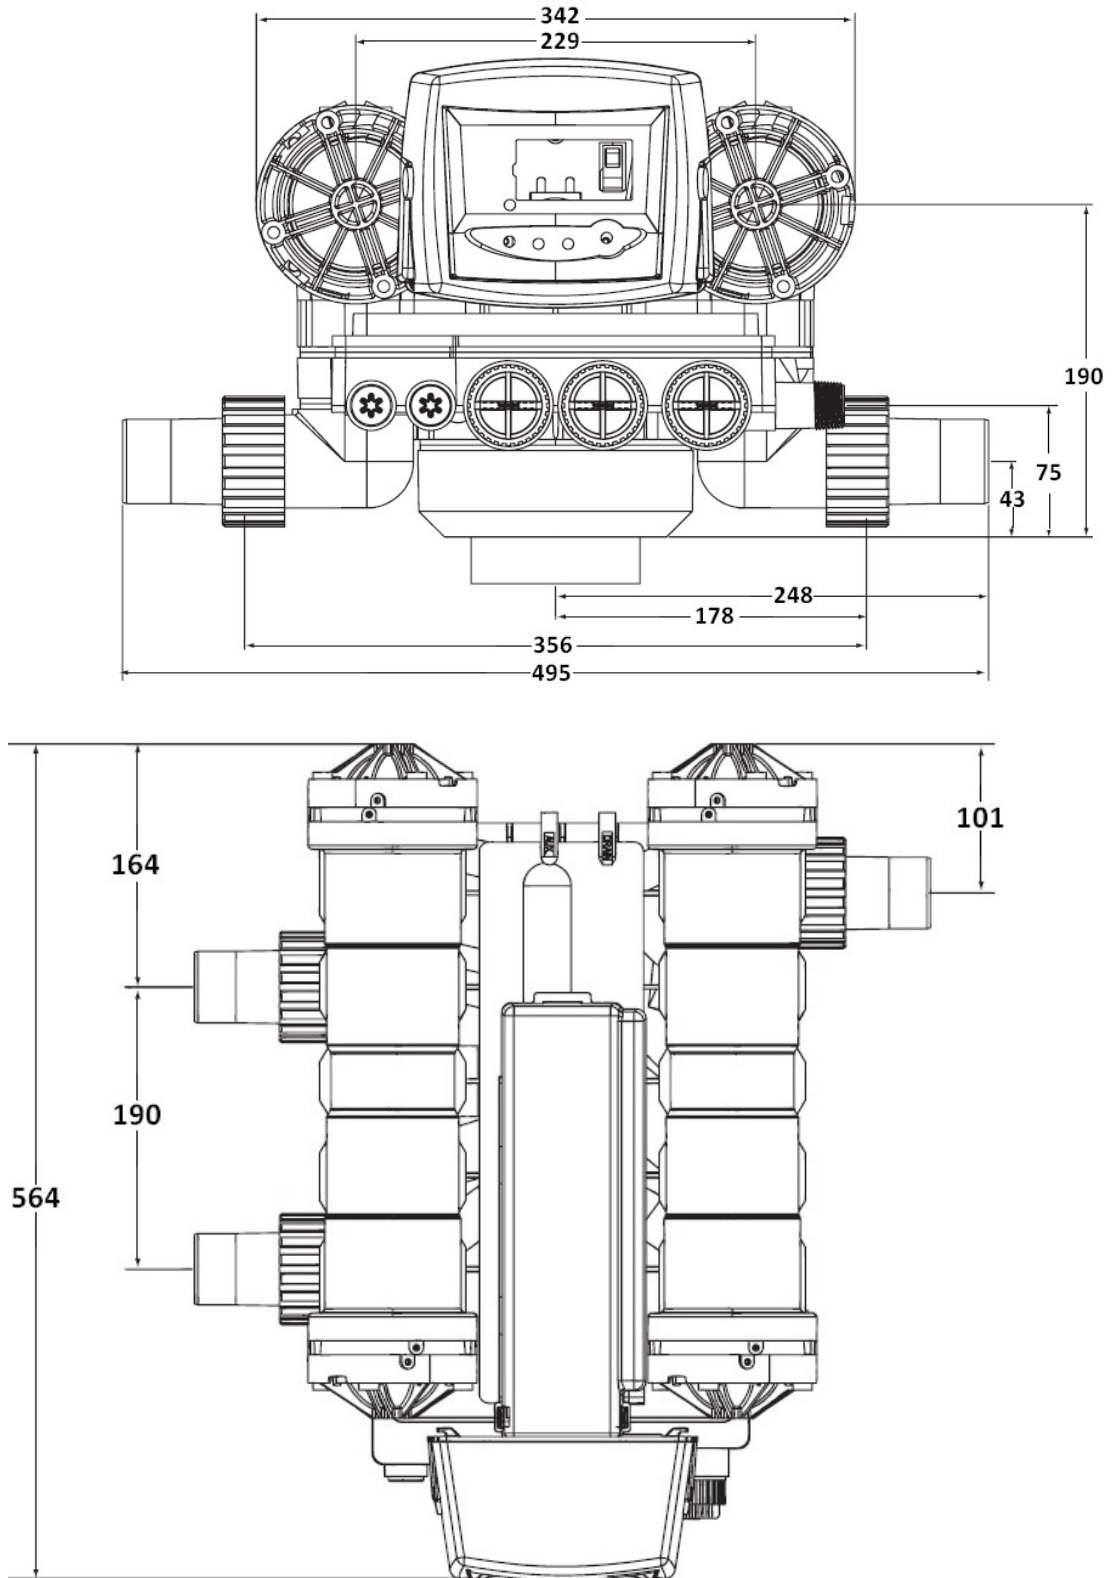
Dimensiones válvula Magnum CV 1½”
